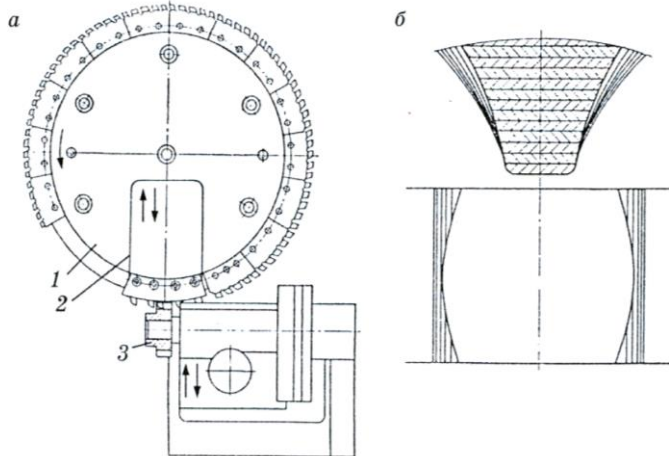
Кругодиагональное протягивание зубчатых колес: а – схема станка; 1 – диск протяжки; 2 – ползун; 3 – зубчатое колесо; б – схема резания
